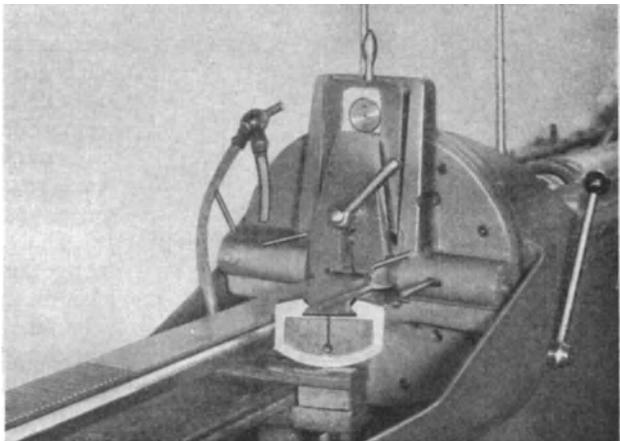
Räumzeug für Waagerechträummaschine (Forst).
